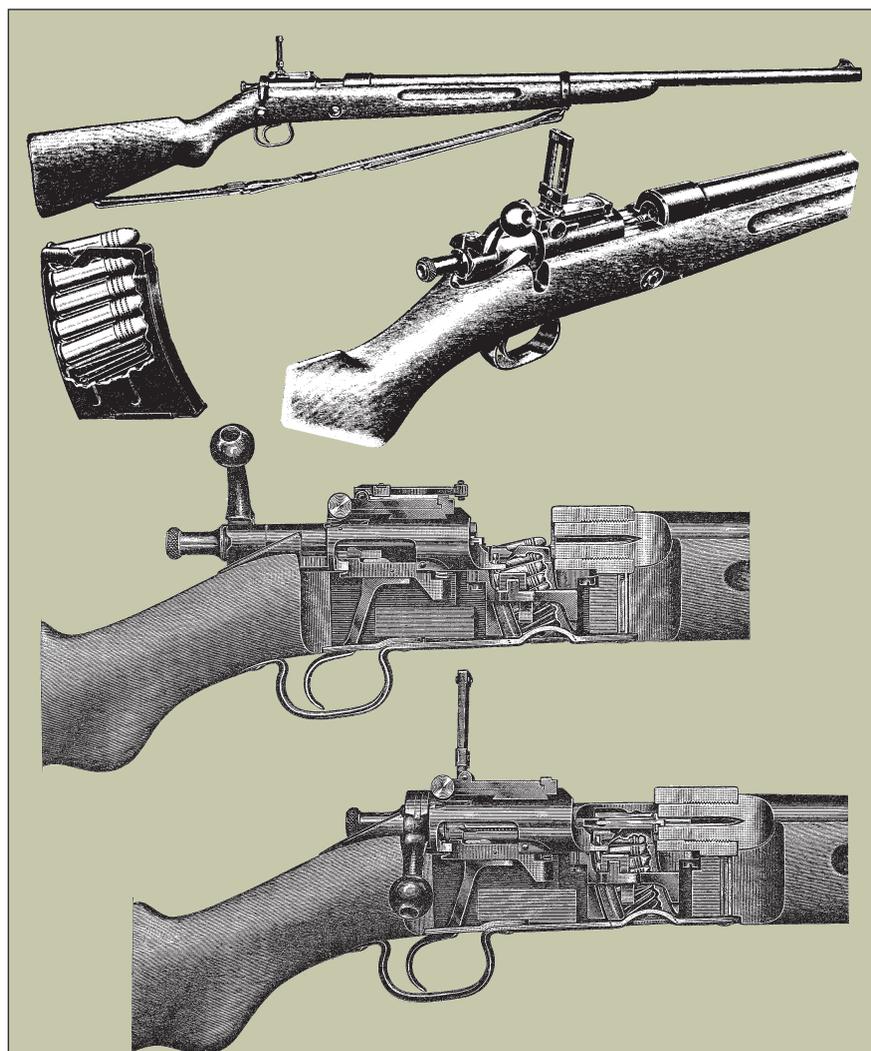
Малокалиберная винтовка системы Винчестер, модель 52 и ее механизм в положении открытого и закрытого затвора
